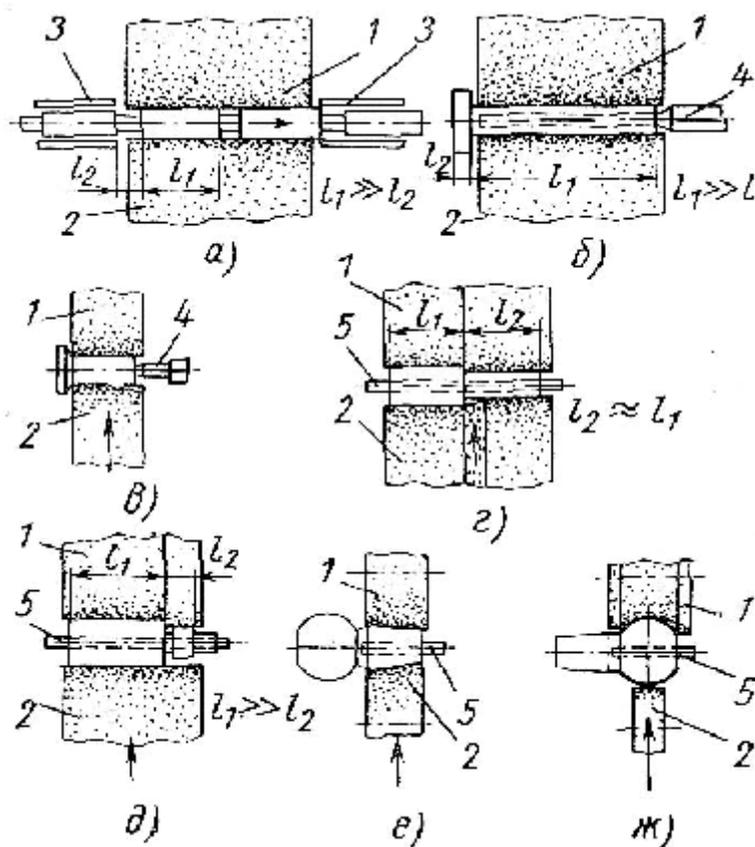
Схемы процессов бесцентрового шлифования с поперечной подачей: 1 – шлифовальный круг; 2 – ведущий круг; 3 – направляющая линейка; 4 – упор; 5 – опорный нож, [6]
